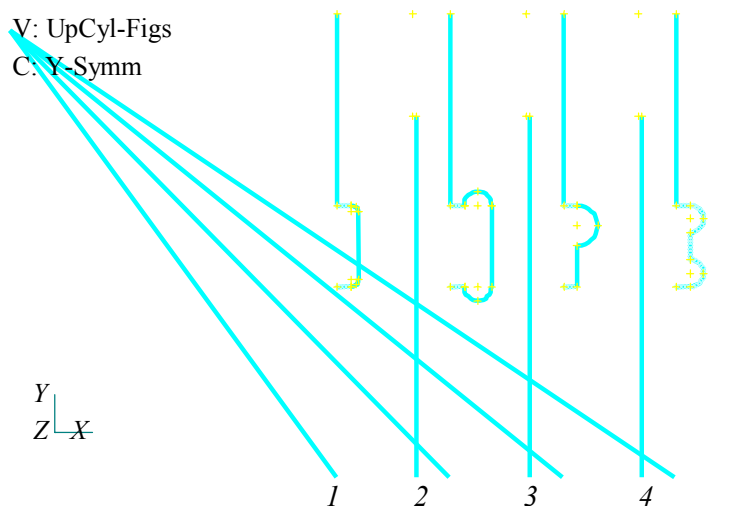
Варианты проточек верхней части корпуса цилиндрического сосуда давления:
